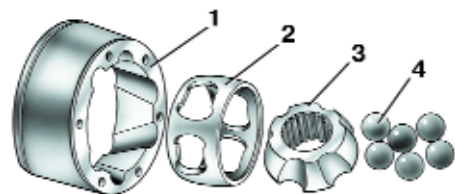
Детали внутреннего шарнира: 1 – корпус шарнира; 2 – сепаратор; 3 – обойма; 4 – шарики
